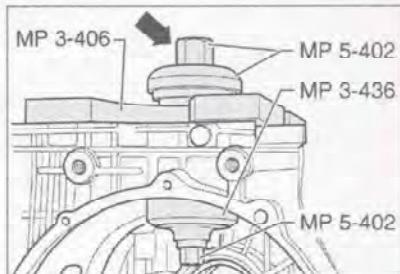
Снятие наружной обоймы большого роликоподшипника.
